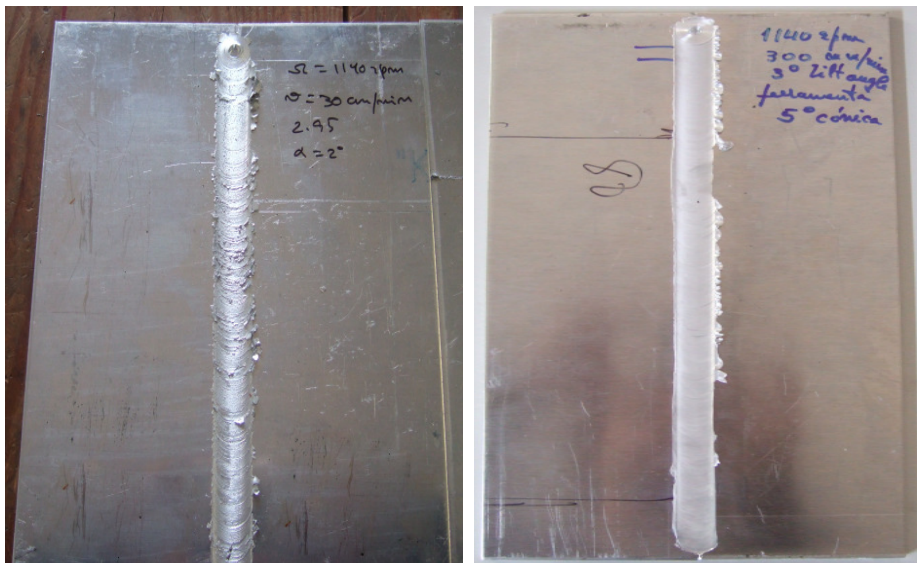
Exemplo de soldaduras efectuadas
